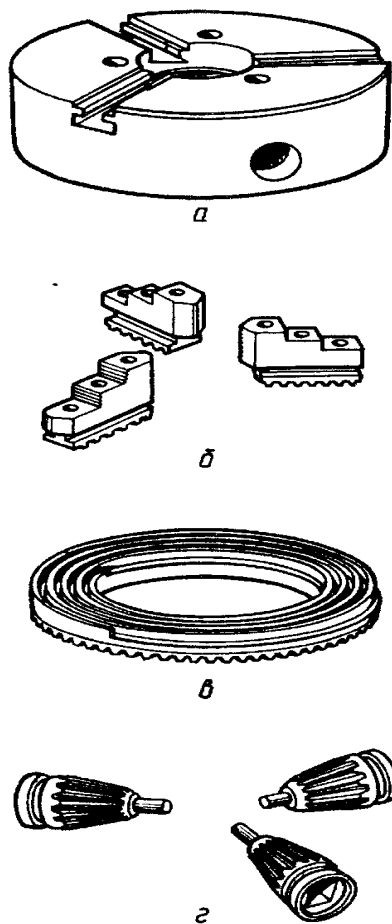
Деталі трикулачкового самоцентруючого патрона: а - корпус; б - кулачки; в - зубчасте колесо („планетарка”); г - привідні шестерні
